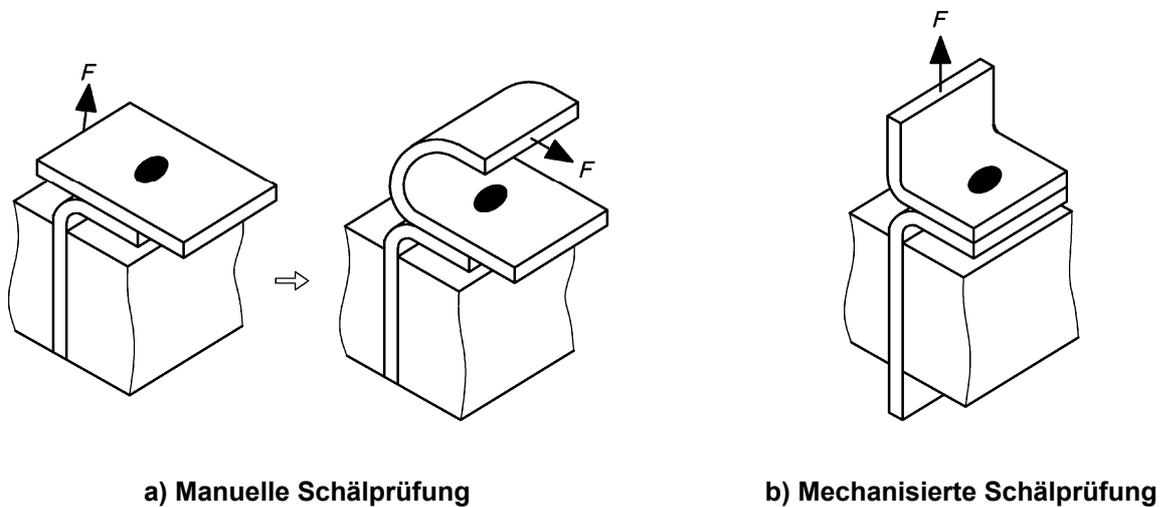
Schälprüfung an Widerstandspunkt- und Buckelschweißverbindungen
